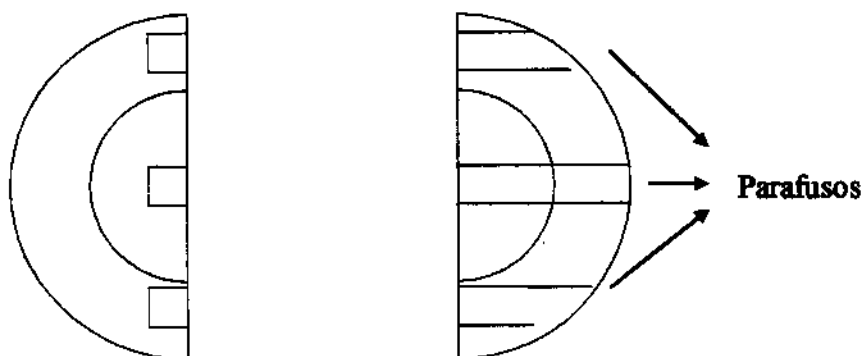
Desenho do molde de ferro utilizado para o fabrico dos tarugos.
